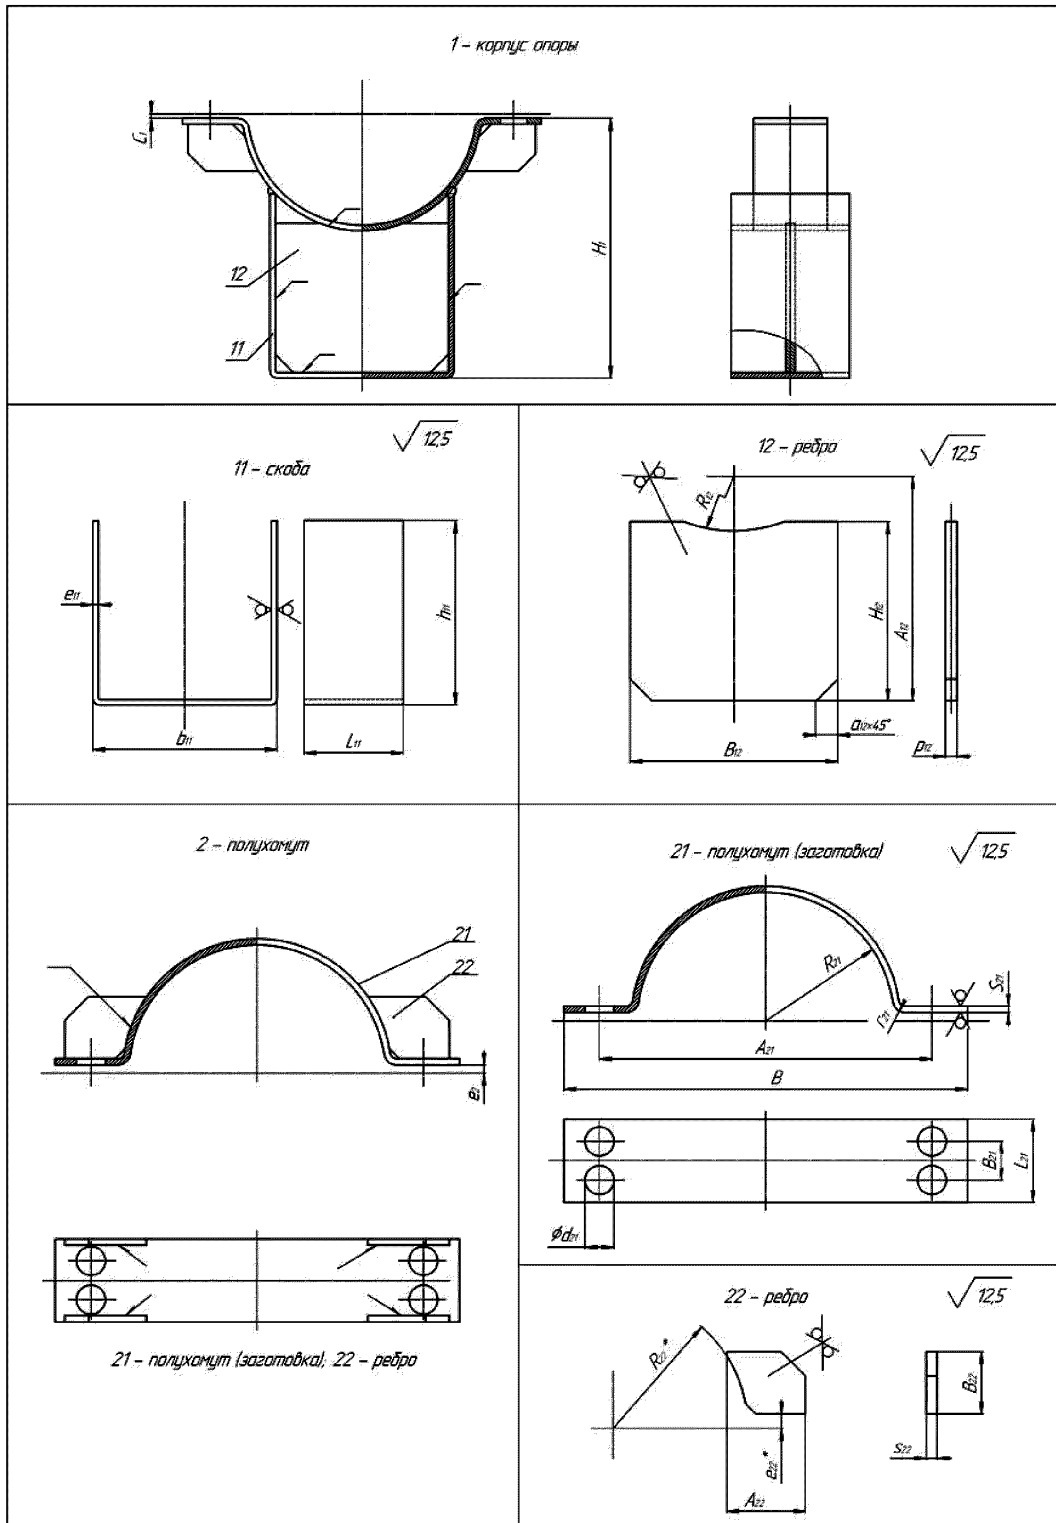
Детали изделий 01-XXXX-S-1C-03-A,
